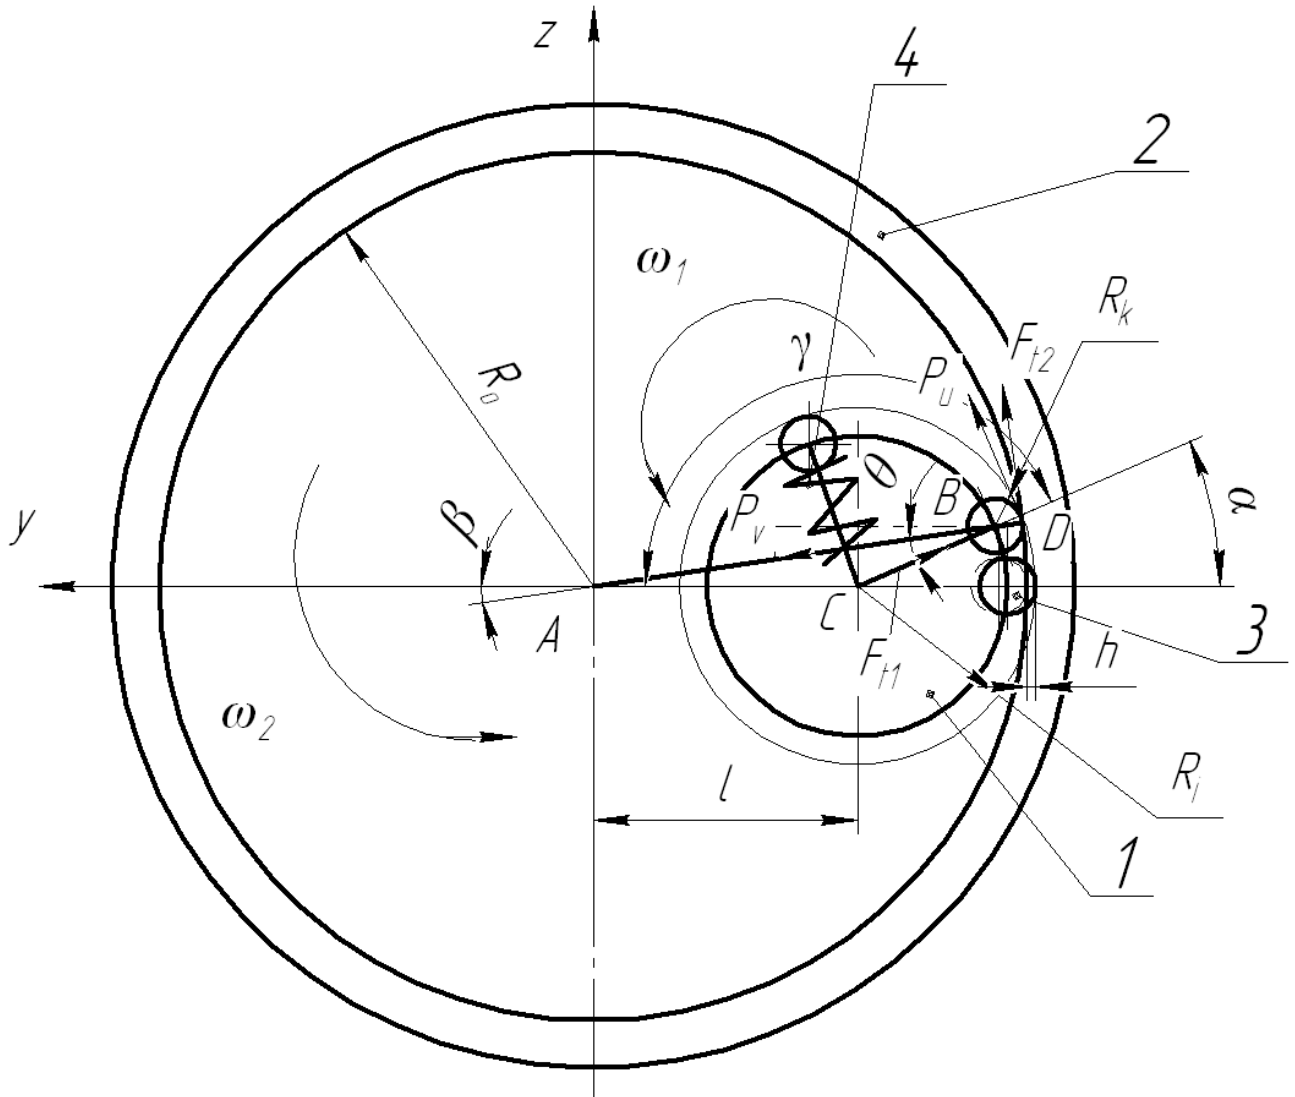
Розрахункова схема для встановлення взаємозв'язку конструктивних та силових параметрів процесу зміцнення поверхні отвору кульками: 1 – оправка, 2 – заготовка з отвором; 3 – кулька; 4 – пружина стиску
